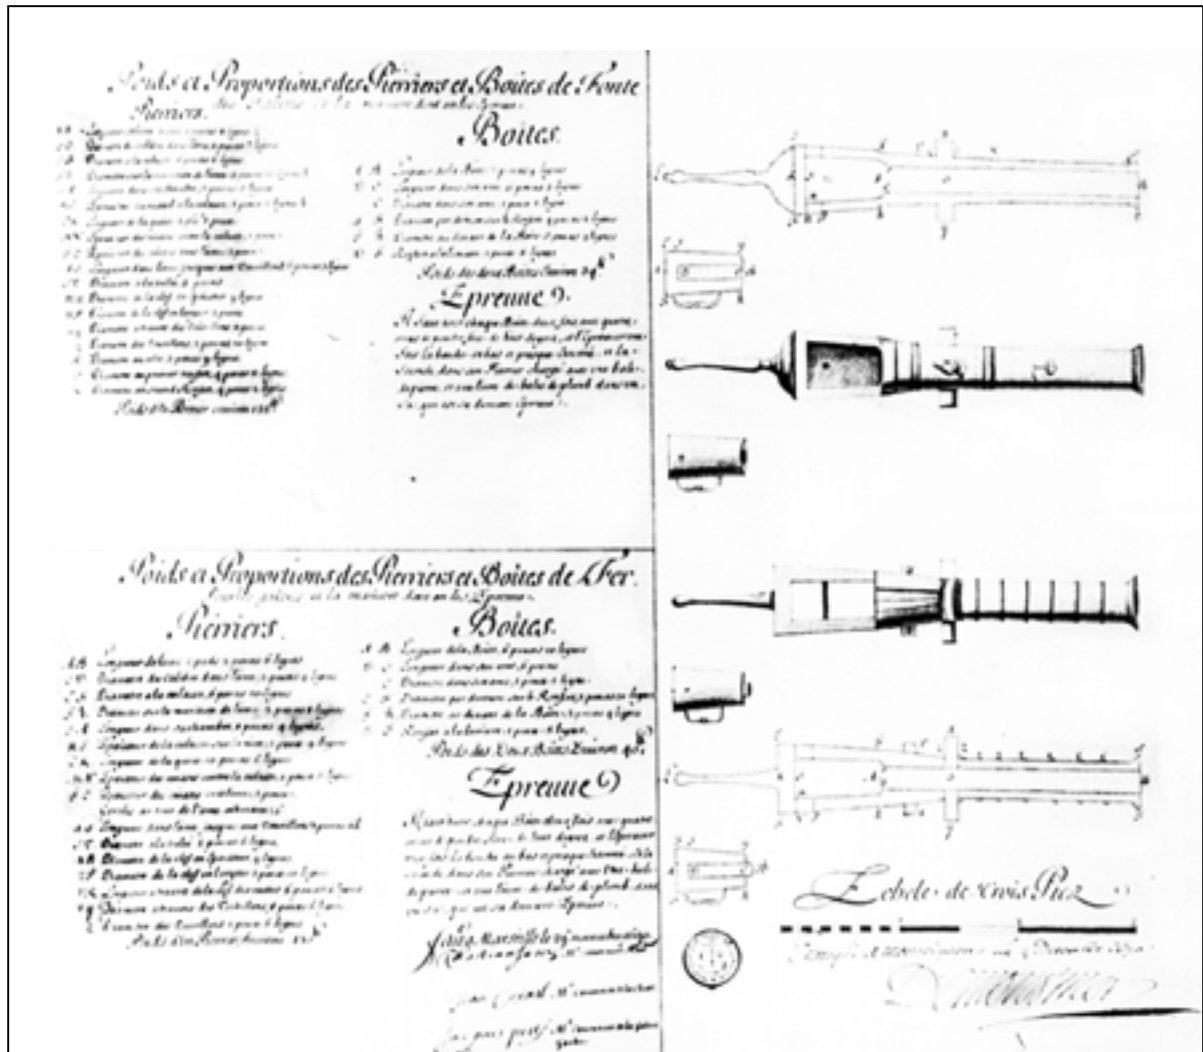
Plan et proportions des pierriers et boîtes en fer et de fonte pour les galleres..., Marseille, 1690.
